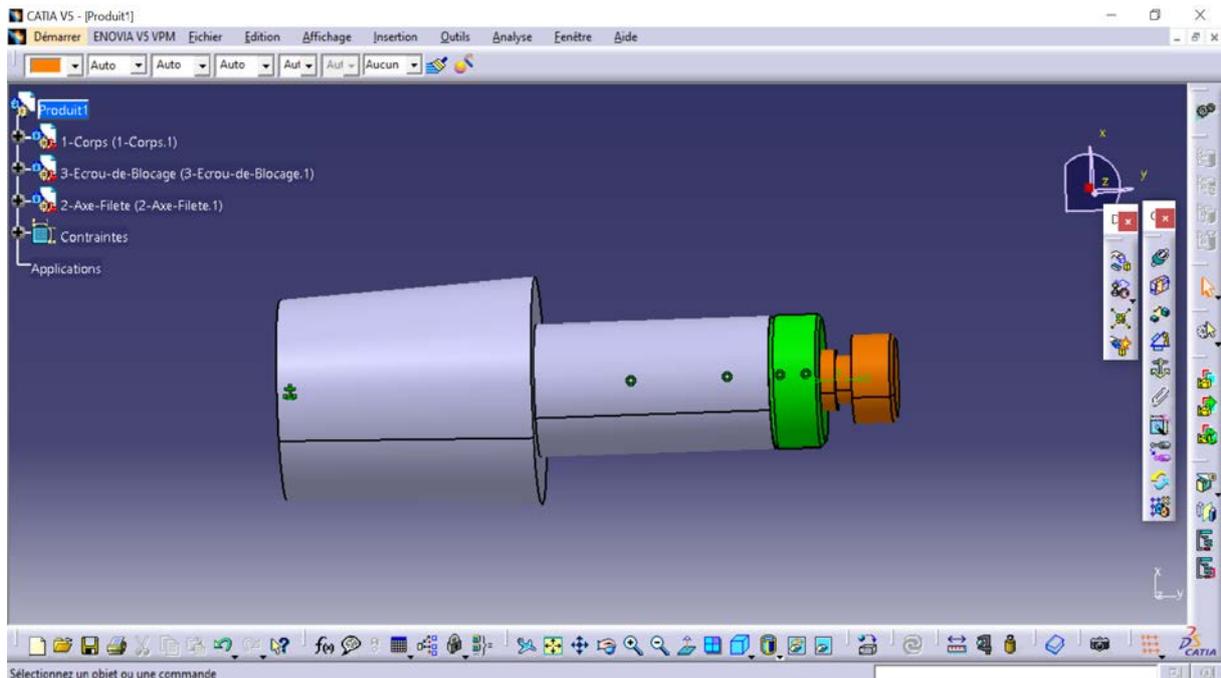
Assembly Design des Pièces 1, 2 et 3 [1], [2]
